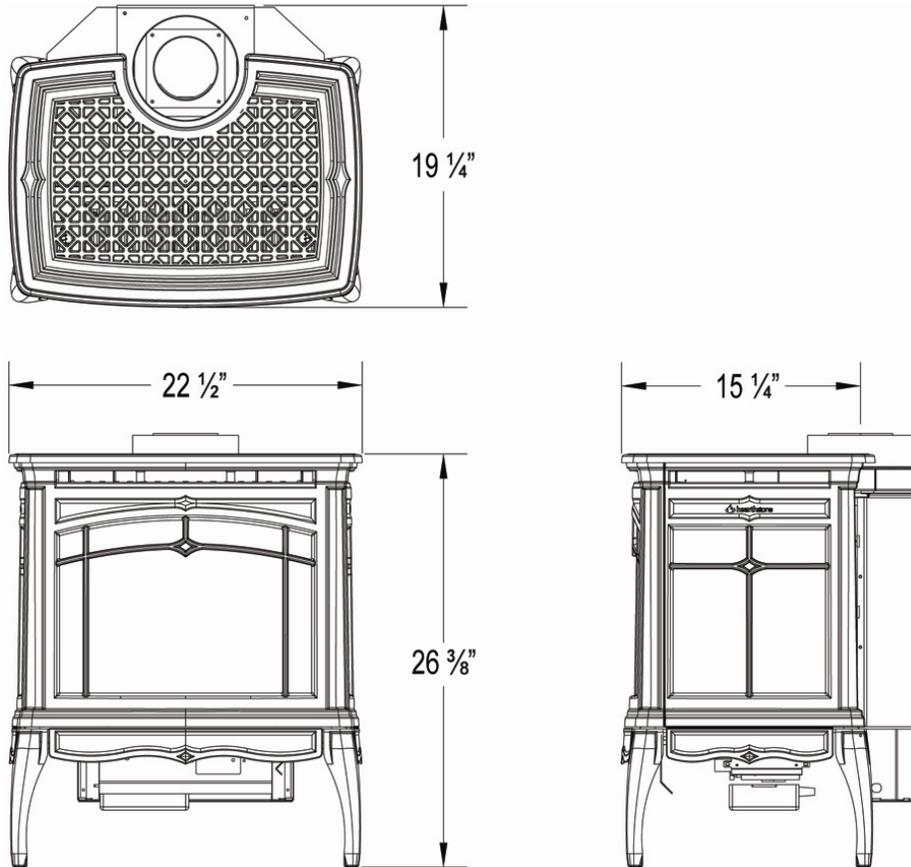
Dimensions du Modèle 8762 (en pouces)
